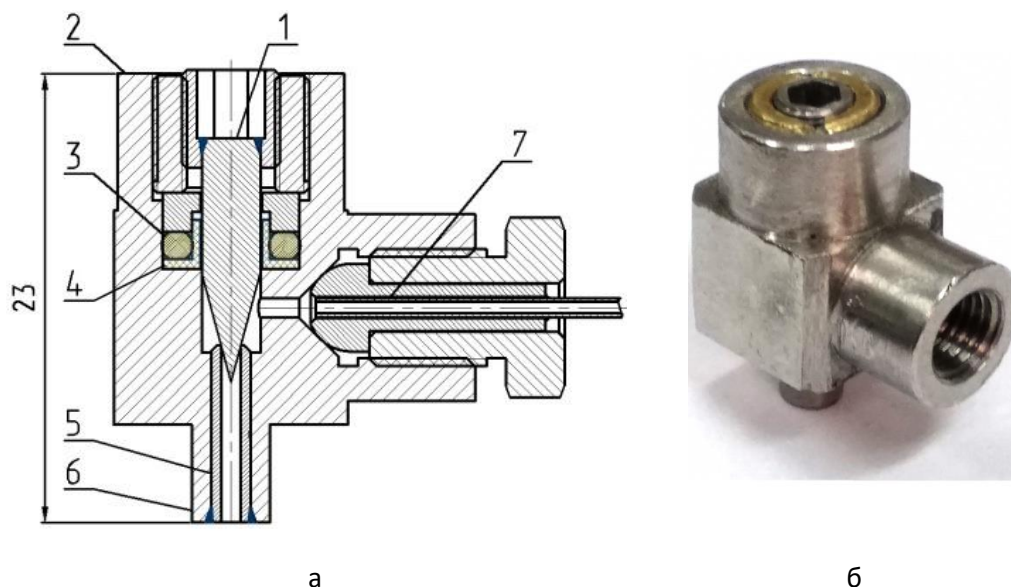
Конструкция (а) и внешний вид (б) вентиля
